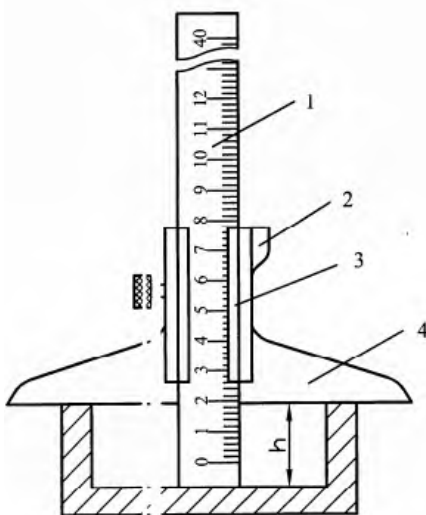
Штангенглубиномер: схема измерения [2]
